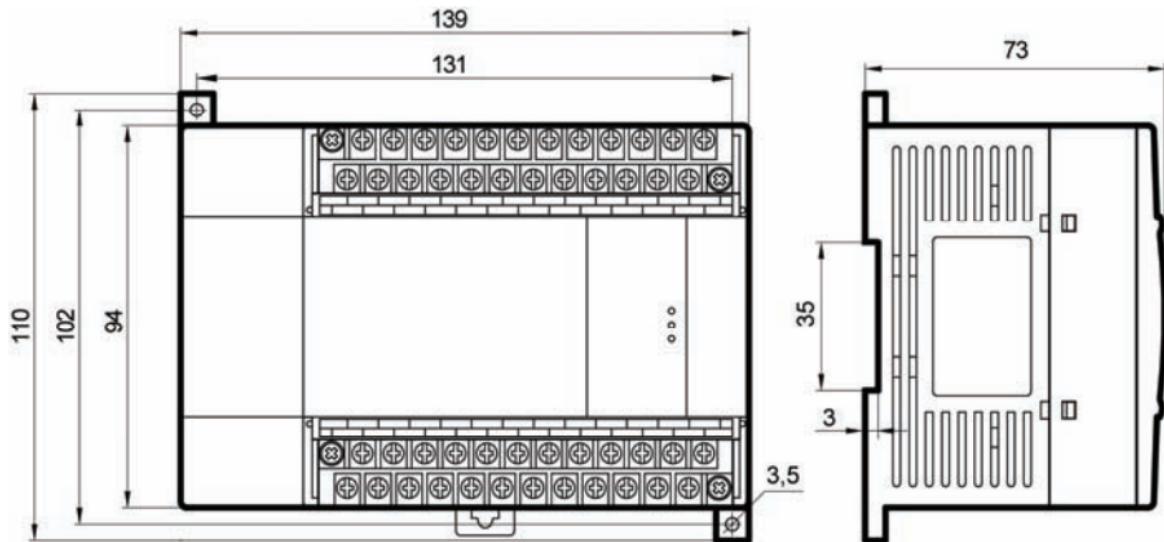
Габаритный чертеж ОВЕН МВ110-224.4ТД
